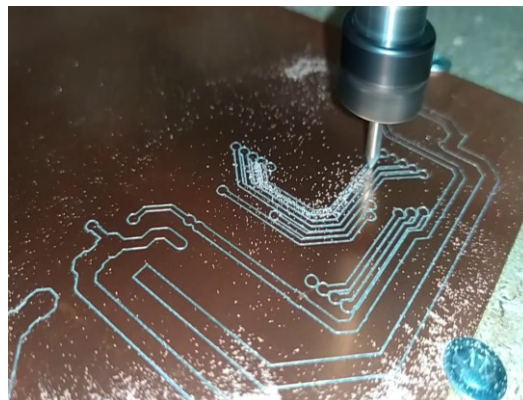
Фрезерование МПП с помощью станка с ЧПУ
